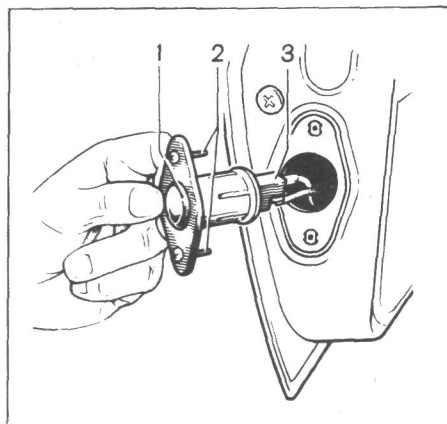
Фонарь сигнализации открытой двери: 1 — корпус рассеивателя; 2 — винты крепления фонаря; 3 — патрон лампы
